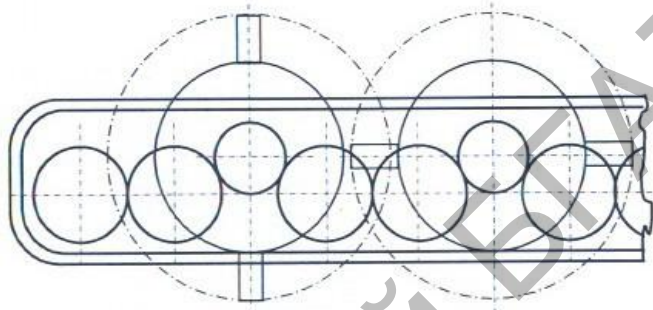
Многороторный рабочий орган с вынесенными вперед осями вращения ротора
